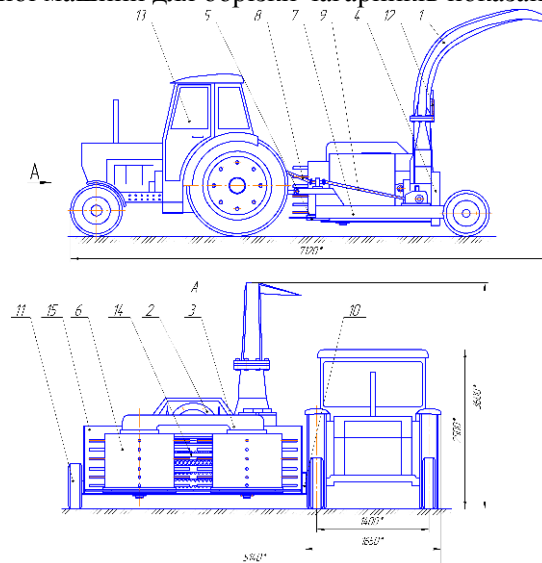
Машина для обрізки чагарників, причіпна: 1 – дефлектор; 2 – подрібнювач; 3 – привод ножового апарата; 4 – првод подрібнювача; 5 – ножовий апарат; 6 – направляюча; 7 – причіпний пристрій; 8 – вал карданний; 9 – вал проміжний; 10 – пристрій шарнірний; 11 – колесо опорне; 12 – механізм повороту дефлектора; 13 – трактор; 14 – вальці прижимні; 15 – щиток направляючий
